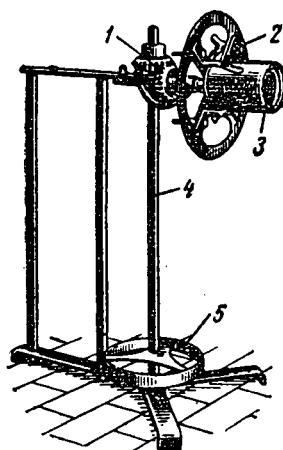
Передвижное приспособление для паяния днищ и обечаек
